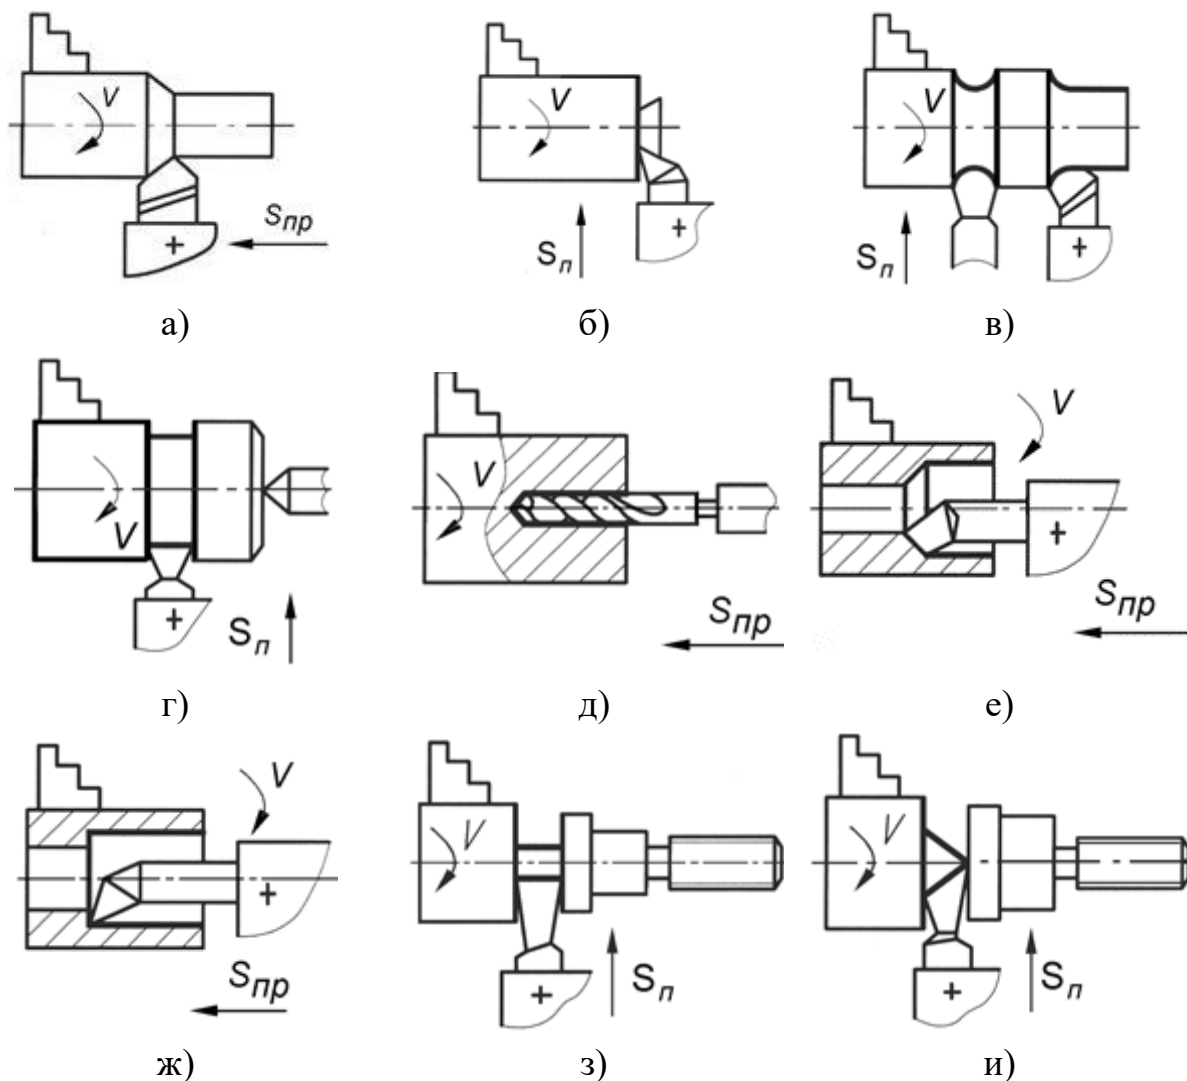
Схемы обработки на токарно-винторезном станке
